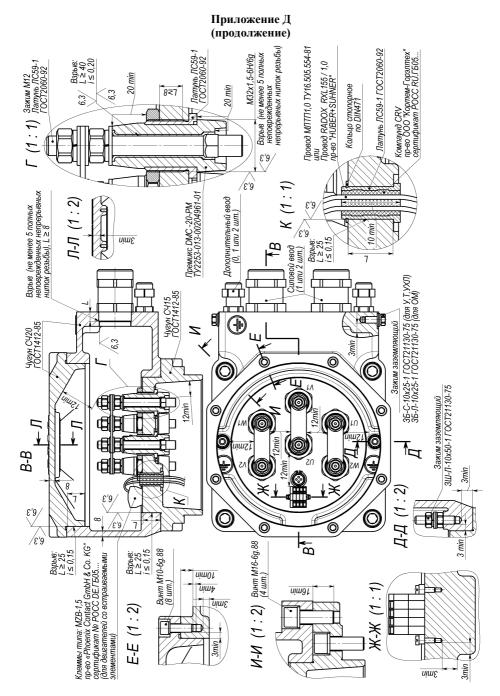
Чертеж взрывозащиты коробки выводов «d» двигателей BA(Б),1PBA 250,280; BRA(Б),1PBRA 280,315
